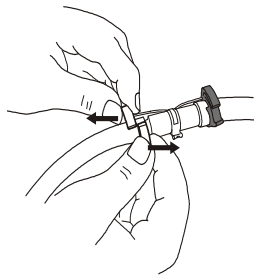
Desserrage d'une bague de serrage du raccord18
